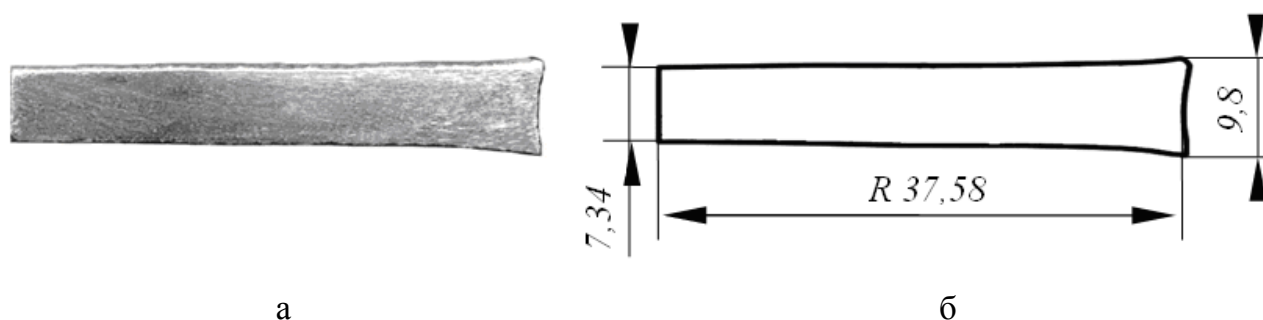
Сечение СВС-прессованной заготовки из сплава TiC–20%Ni.
